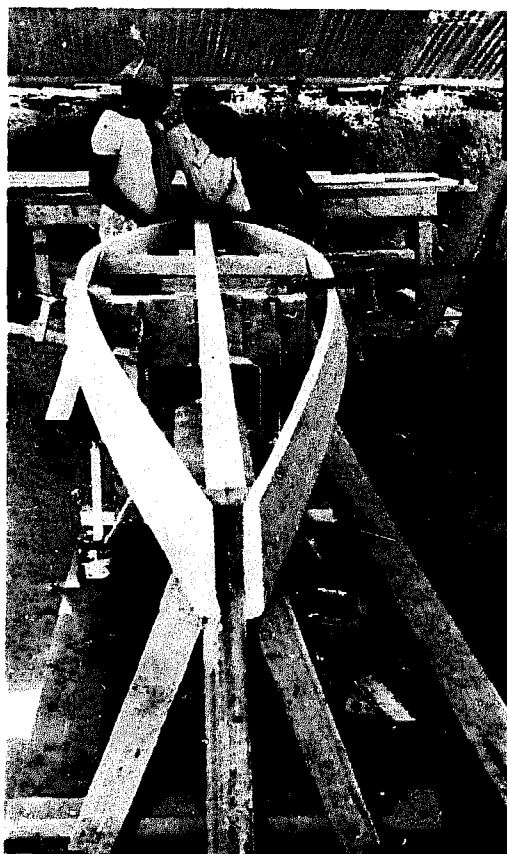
Attraper l'autre bout des bouchains et les presser ensemble au-dessus de la deuxième étrave
